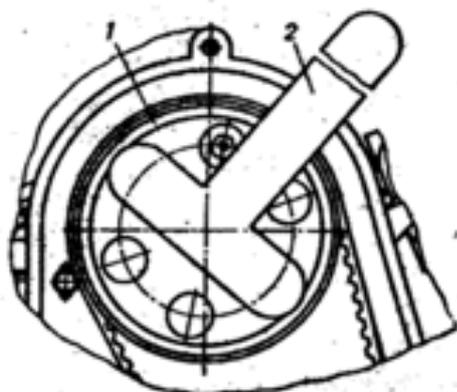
Проворачивание двигателя за шкив распределительного вала при регулировке зазоров в клапанном механизме: 1 - шкив распределительного вала; 2 - ключ M9811-321
